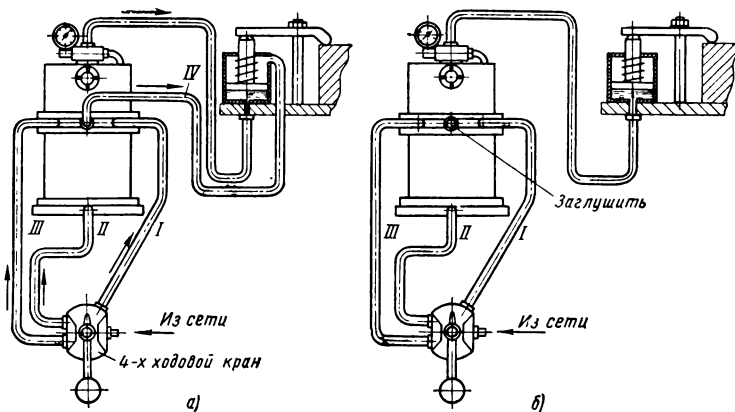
Схема подключений приспособлений с рабочими цилиндрами:
